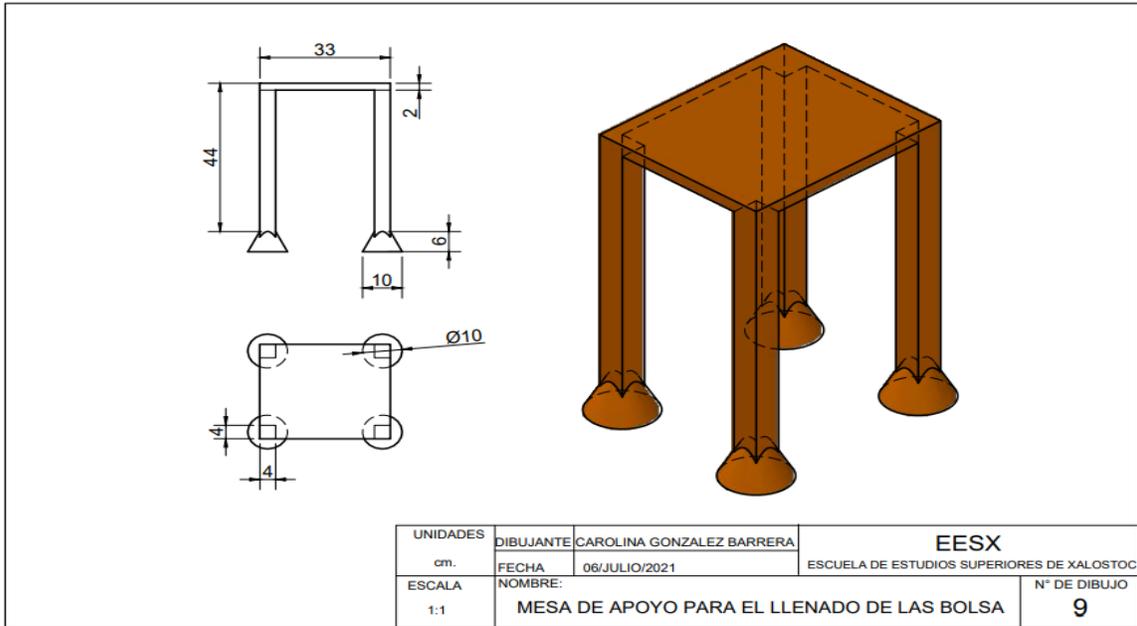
Mesa de apoyo para el llenado de la bolsa
